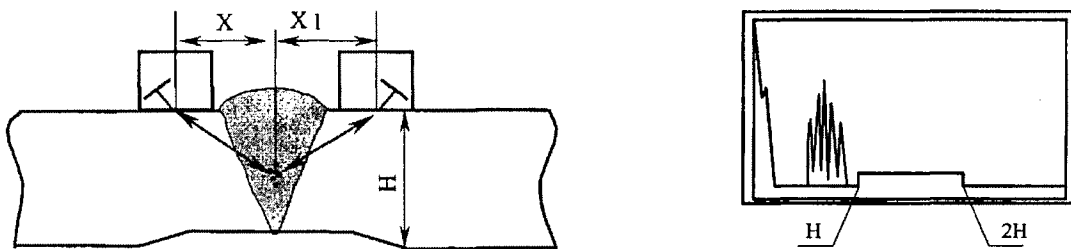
а - Сварное соединение с одиночной порой в сварном шве
